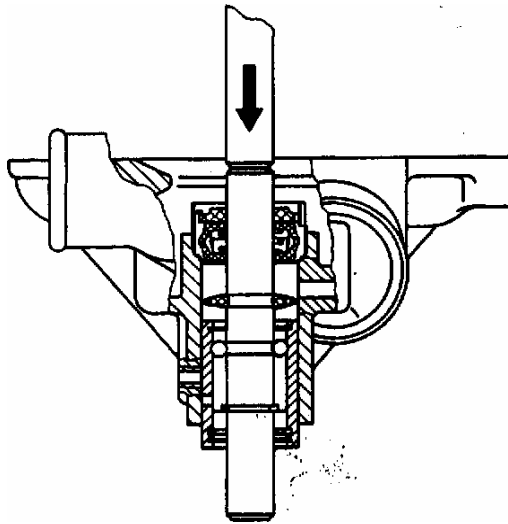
Выпрессовка подшипника с валом водяного насоса
